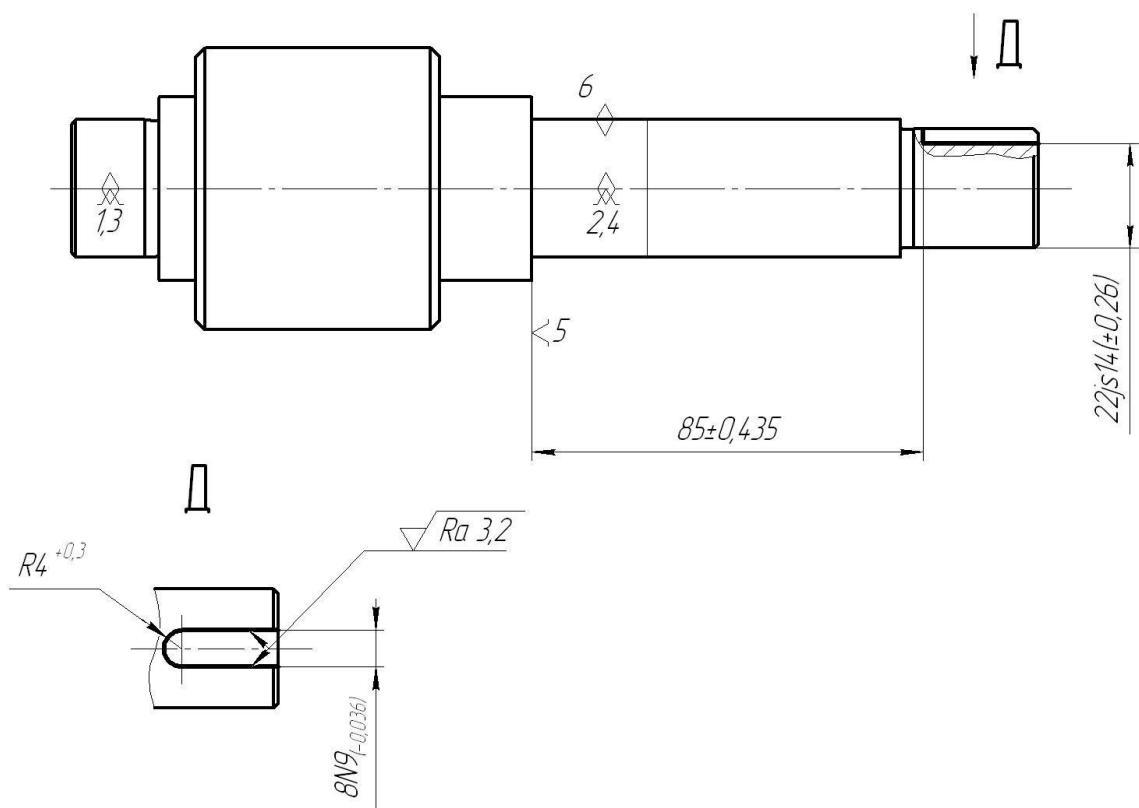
Ескіз операції 030 Шпонково-фрезерна
